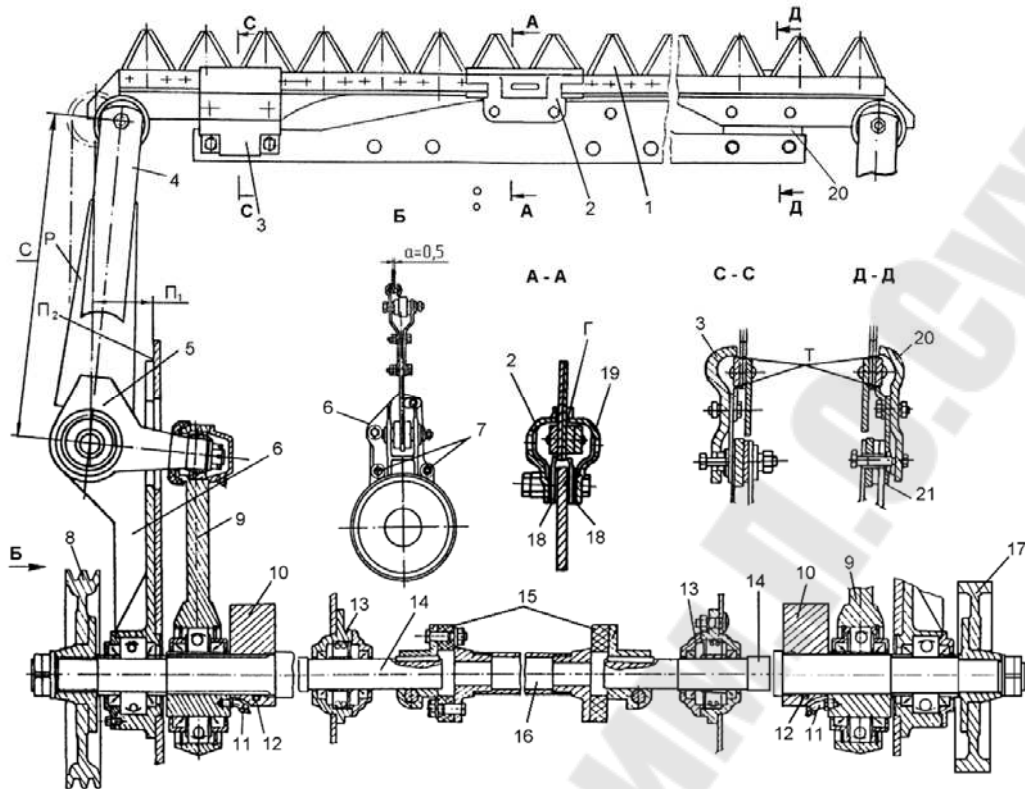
Схема регулировки беспальцевого режущего аппарата жатки для трав:
